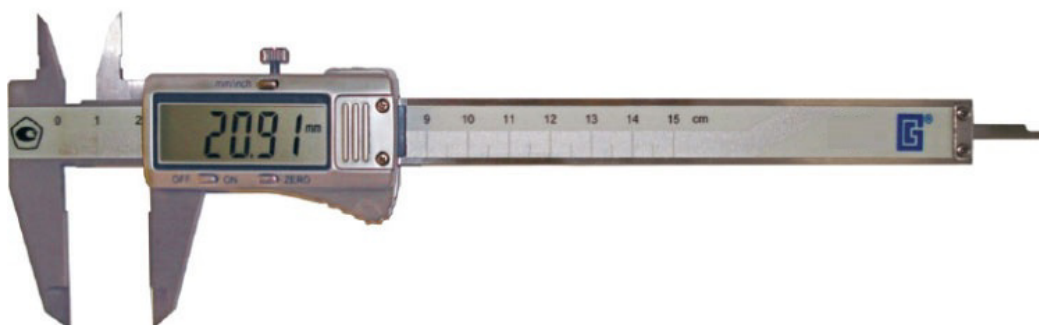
Общий вид штангенциркулей типа ШЦЦ-I.
